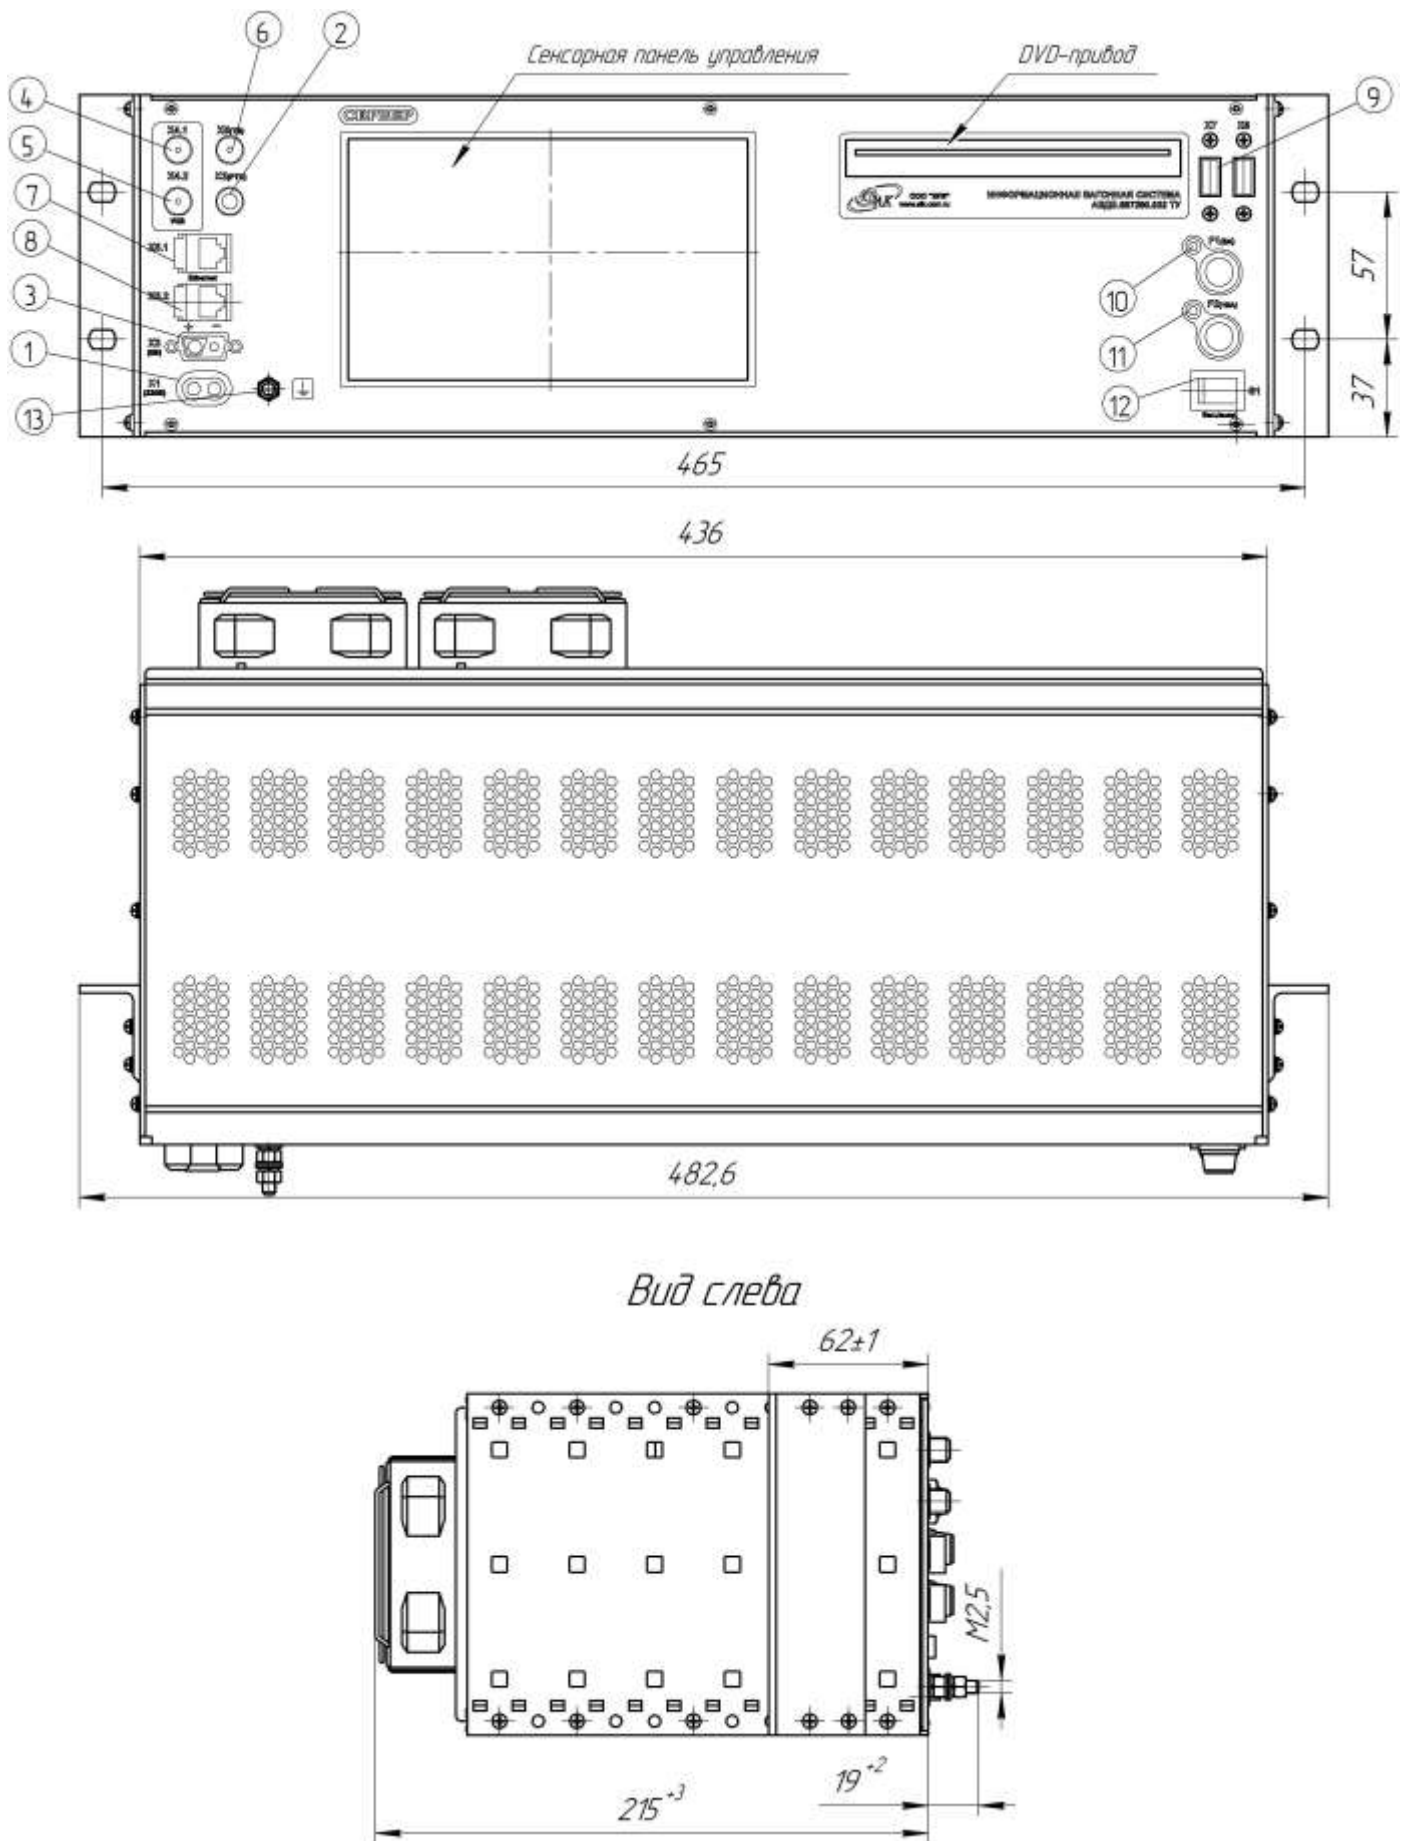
Внешний вид и габаритные размеры сервера-3.01
